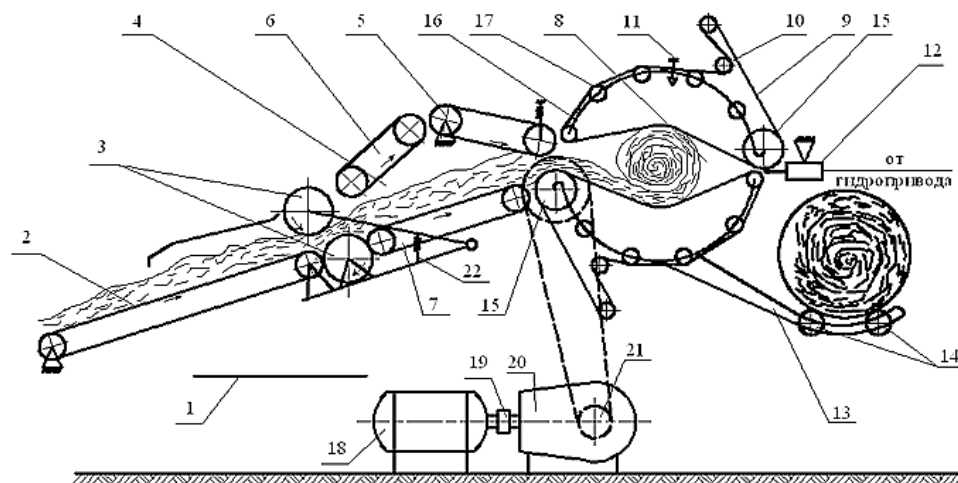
Схема прес-підбирача по формуванню малогабаритних рулонів: 1 – рама; 2 – транспортер; 3 – ущільнюючі вальці; 4 – попередня камера; 5, 6, 7 – робочі транспортери попередньої камери; 8 – пресувальна камера; 9 – ремінний робочий елемент; 10 – натягач; 11 – датчик тиску; 12 – прошивальний пристрій; 13 – підтримуючі важелі; 14 – ролики опорні; 15 – барабан привідний; 16 – корпус прес-камери; 17 – ролики опорні; 18 – електродвигун; 19 – запобіжна муфта; 20 – редуктор; 21 – приводна зірочка.
